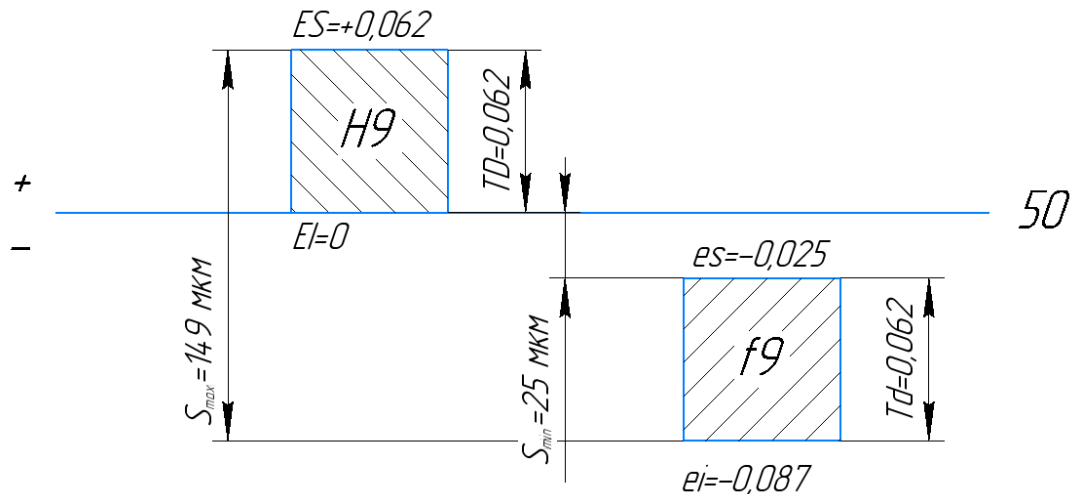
Схема розташування полів допусків для з'єднання отвір-палець $\varnothing 50H9/f$
